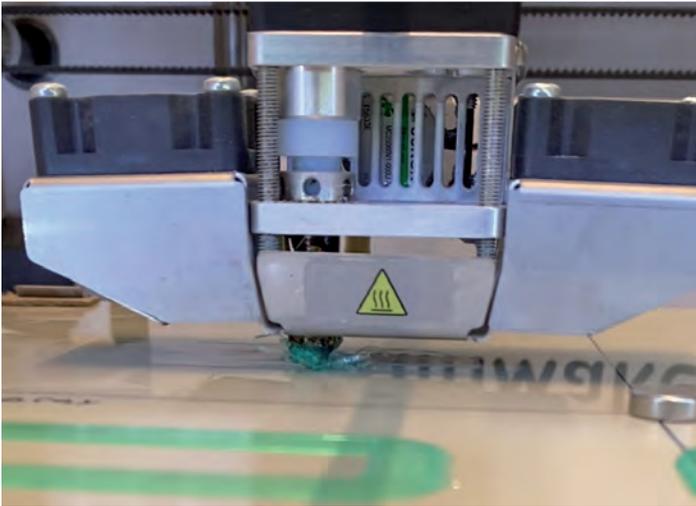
Im Vordergrund ist eine Probe mit guter Haftung zu sehen, und im Hintergrund ein fehlgeschlagener Druck mangels Haftung
